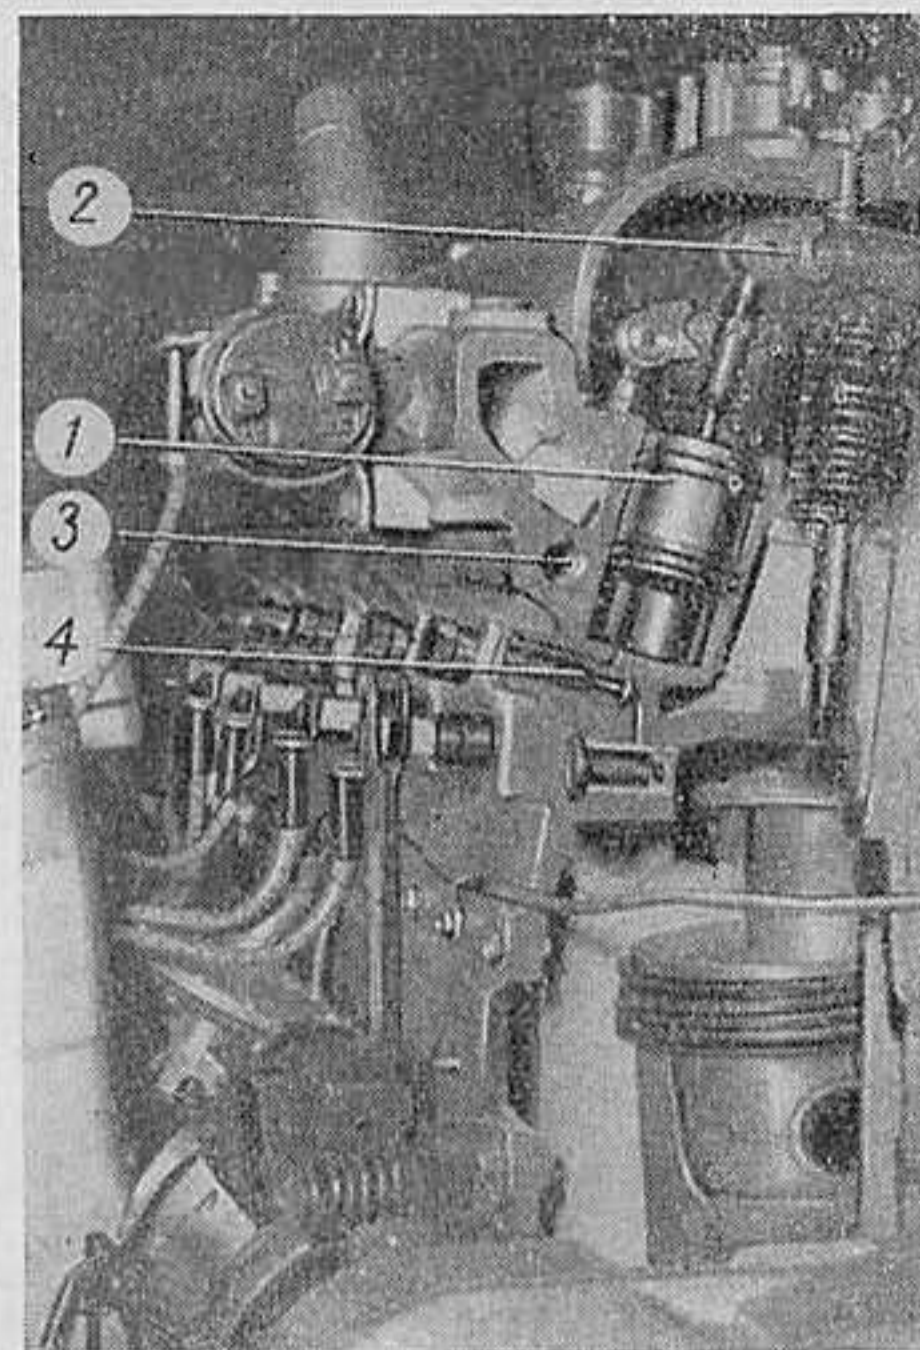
Внешний вид двигателя ЗИЛ-120 с факельным зажиганием.
